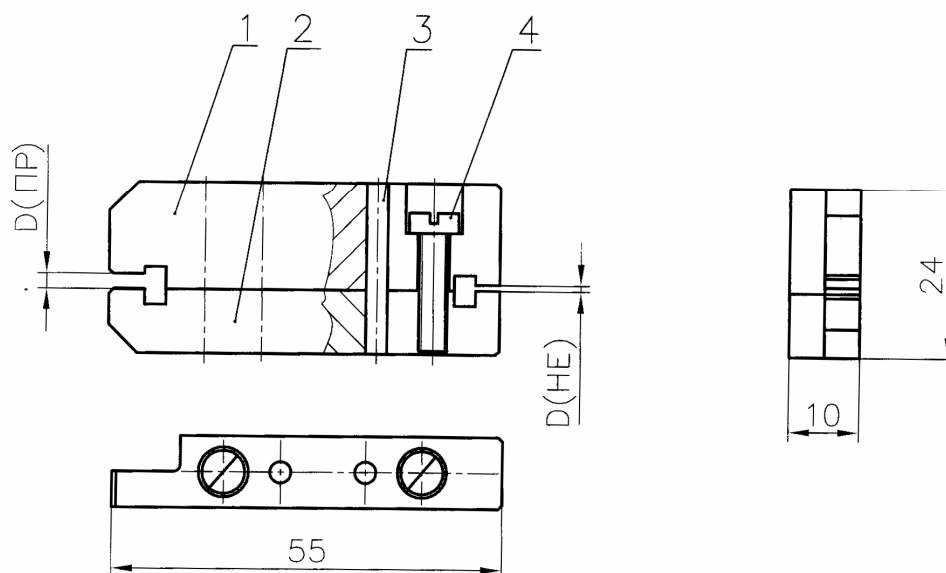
Калибр-скоба гладкий двусторонний:
